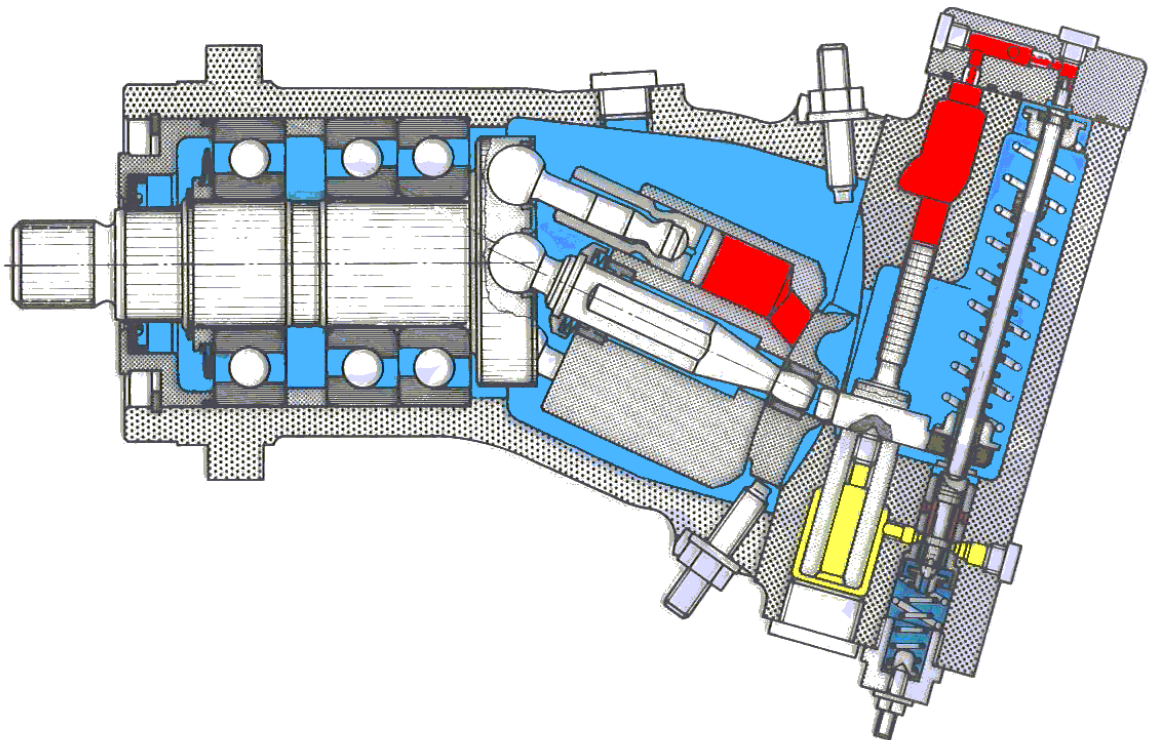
Bomba de pistones axiales con eje inclinado y cilindrada variable.
